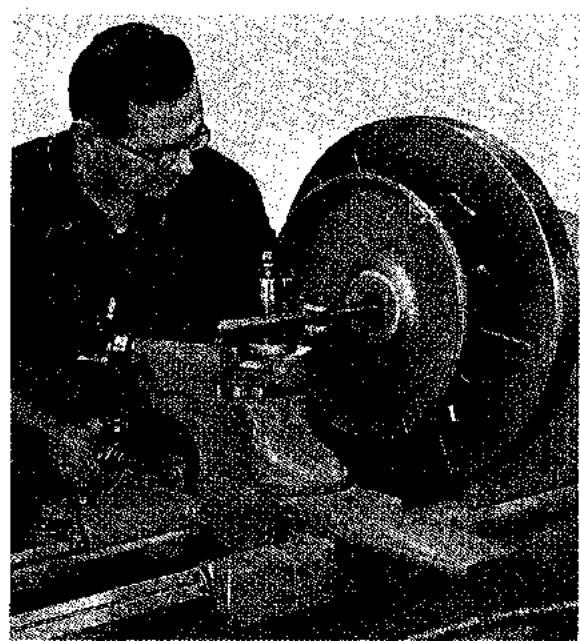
Aplicación del plato frontal (South Bend Lathe Works).
